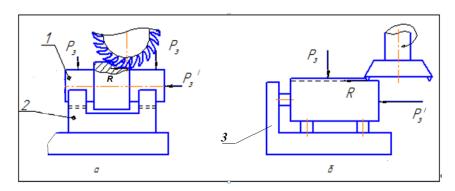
Схемы выбора направления усилия: а – без упора; б – с упором
